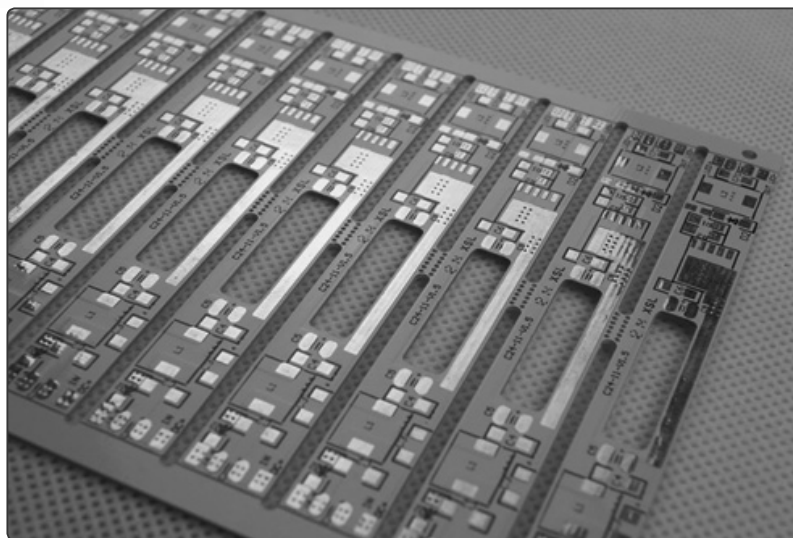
Estañado de PCB, técnica de aislamiento y protección
